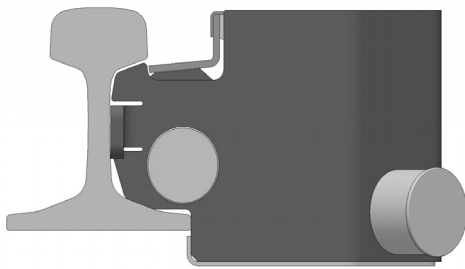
Type SK420-017 (Schienenprofil UIC54; geschraubt/geschweißt)
